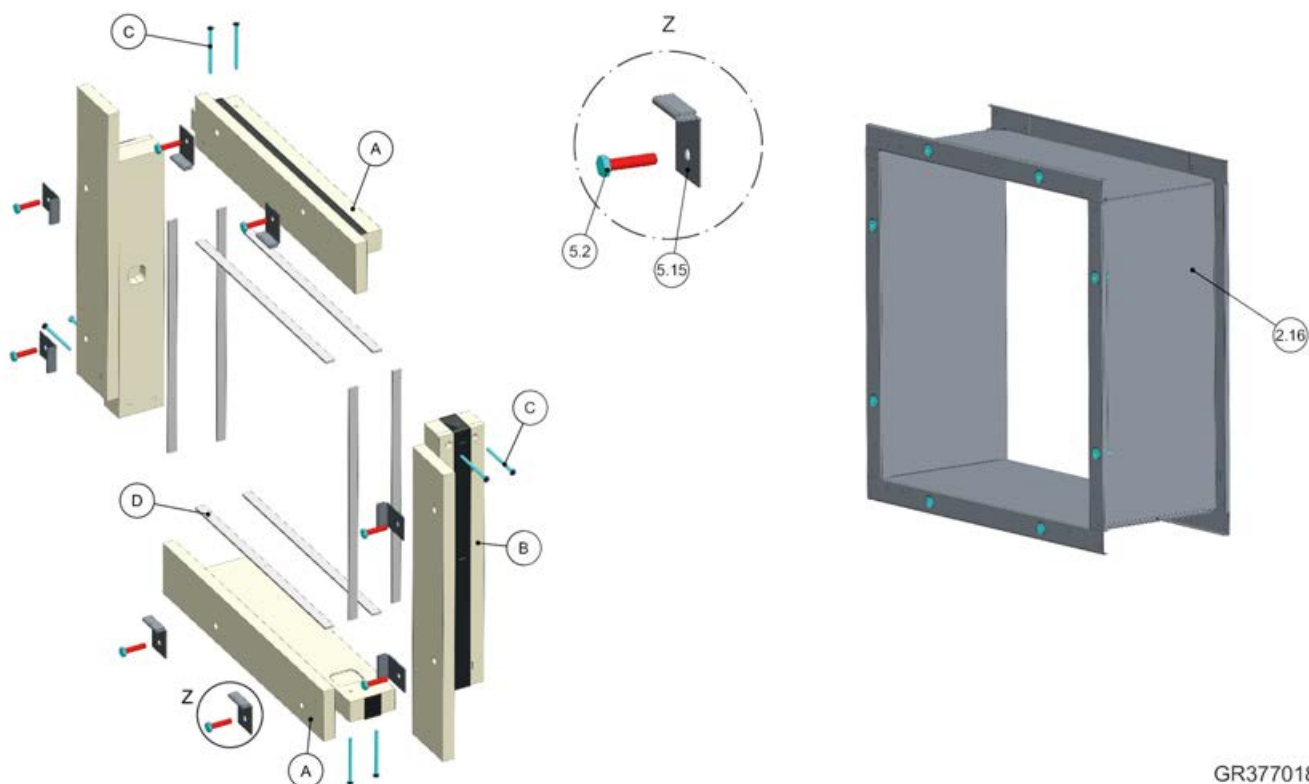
Kit d'installazione EW per installazione a secco con controtelaio di montaggio – pacchetto di fornitura
